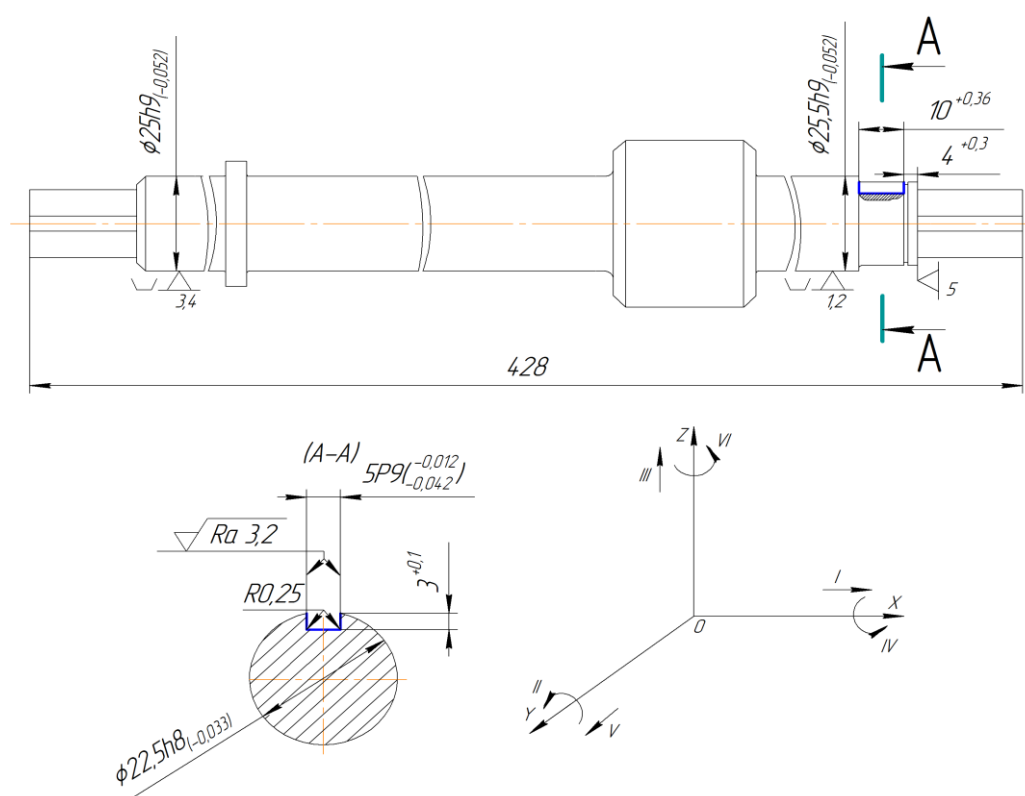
Схема базирования заготовке на вертикально-фрезерной операции
